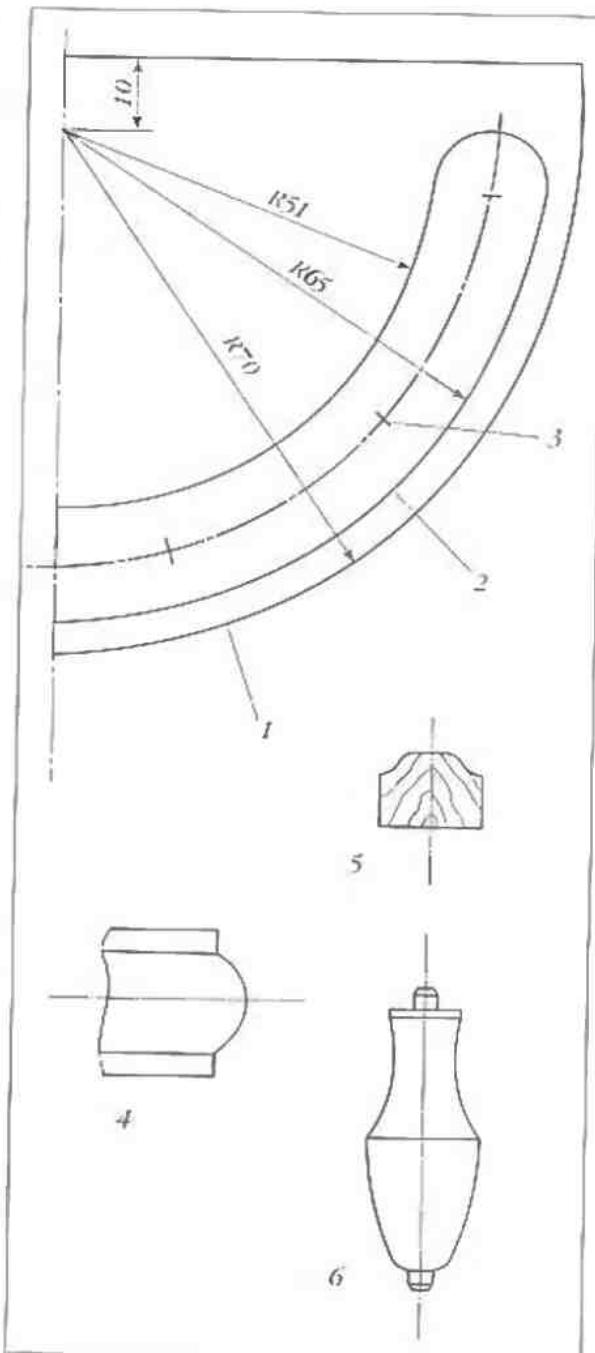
Шаблон полочки-балкончика (масштаб 1:1): 1 - контур платформы; 2 - контур пирса; 3 - места установки балок; 4 - профиль платформы; 5 - сечение пирса; 6 - балка
